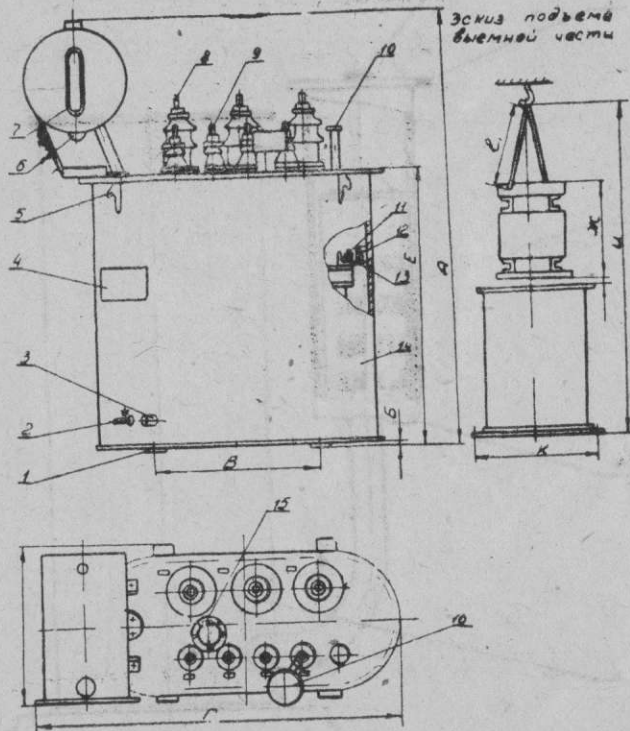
1-пластина; 2-заземление; 3-пробка для заливки и отбора пробы масла; 4-щиток мощности; 5-крюк для подъема трансформатора; 6-воздухоосушитель; 7-маслоуказатель; 8-ввод ВН; 9-ввод НН; 10-ртутный термометр; 11-гайка; 12-скоба; 13-пластина; 14-бак; 15-переключатель; 16-предохранитель (устанавливается по требованию заказчика).
